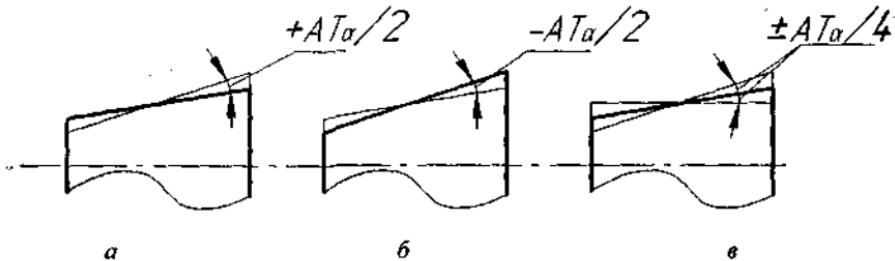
Типы расположения полей допусков для угла конуса:
